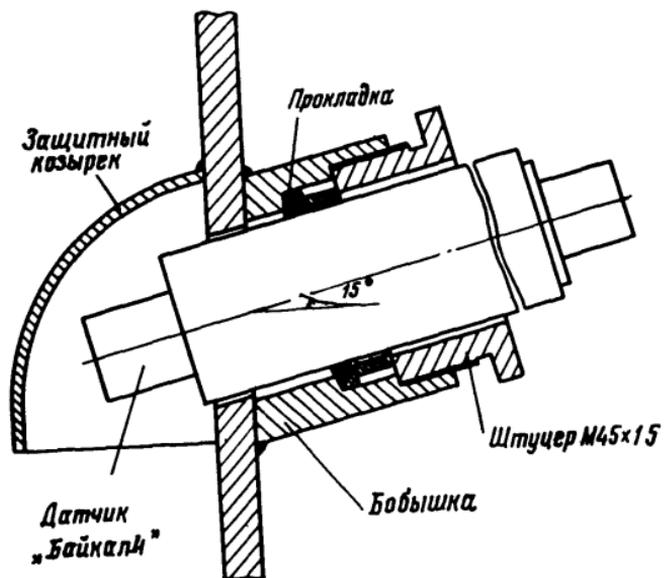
Установка датчика "Байкал-4" в стену камеры
